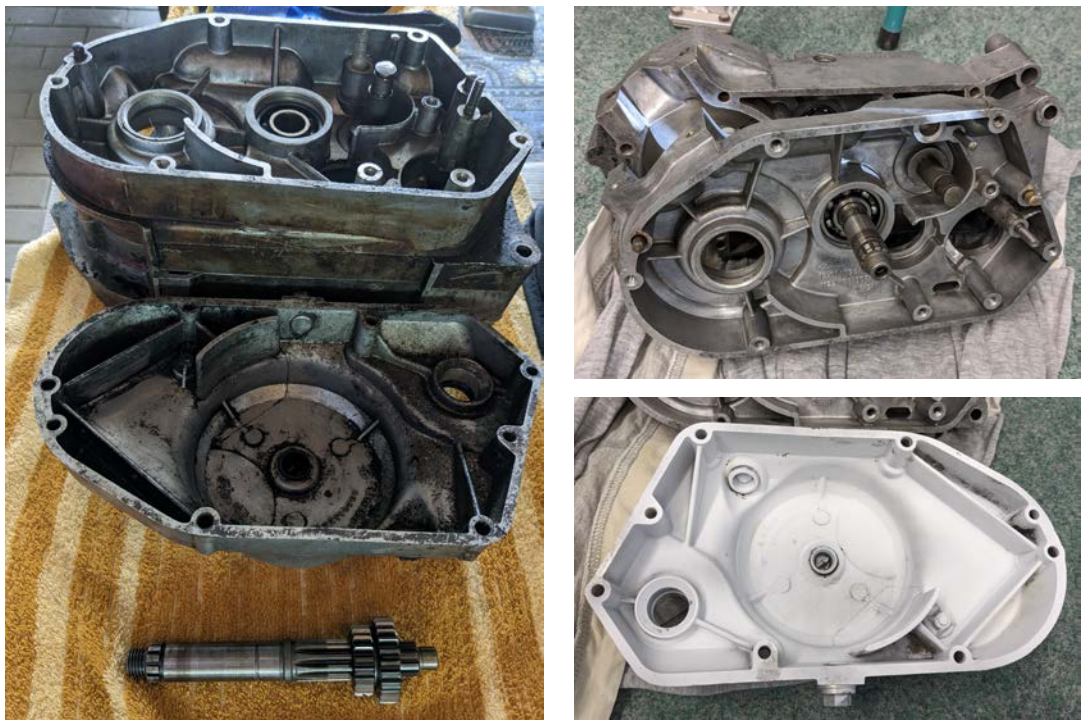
ausgebaute und gereinigte Gehäuseteile des M541 Motor [46]
